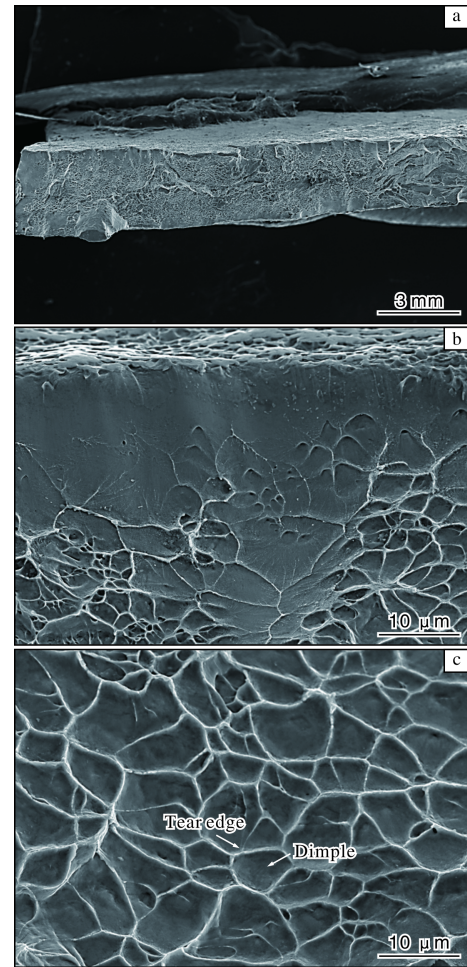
TC17/Ti60 合金激光焊接接头的拉伸断口形貌
